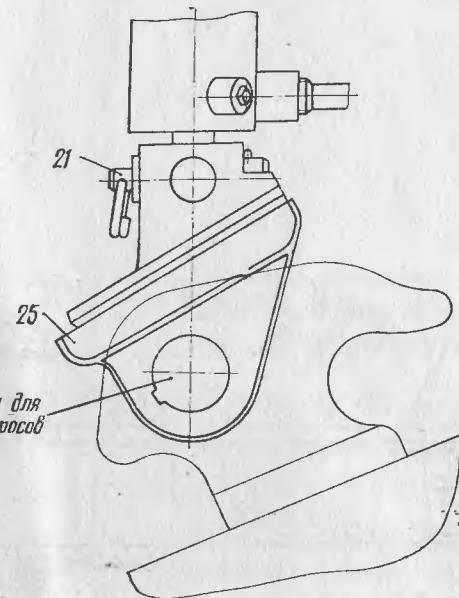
Проверка момента срабатывания сдающего звена подъемного механизма:
